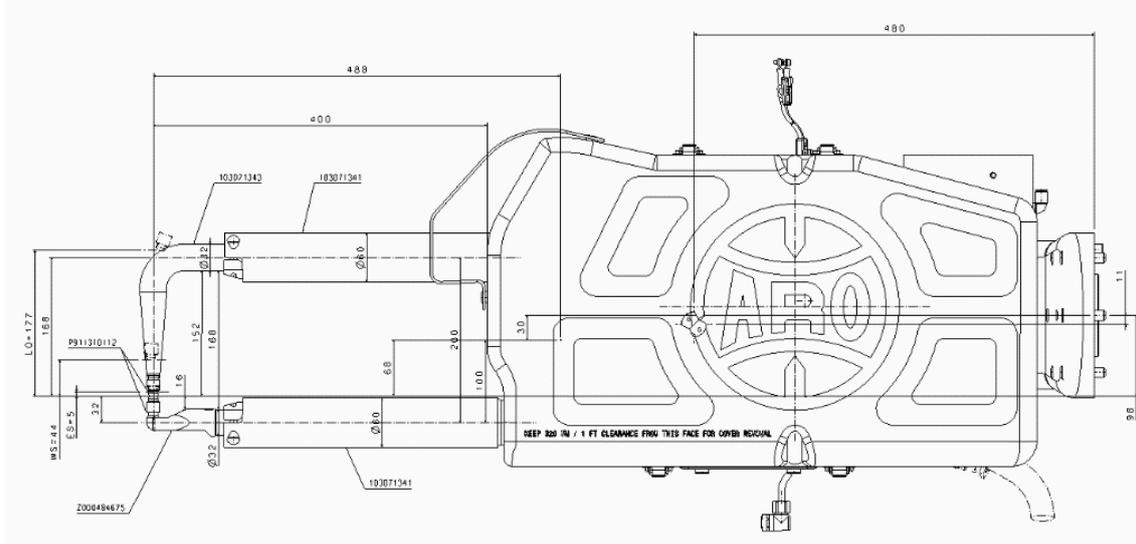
Imagen croquis pinza de soldadura ARO 3G.
